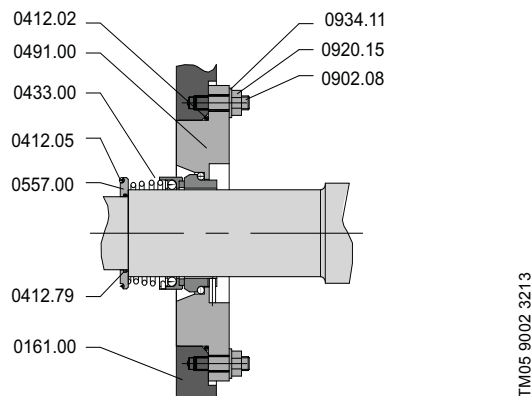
Cierre mecánico sencillo, asiento en cierre de cartucho
